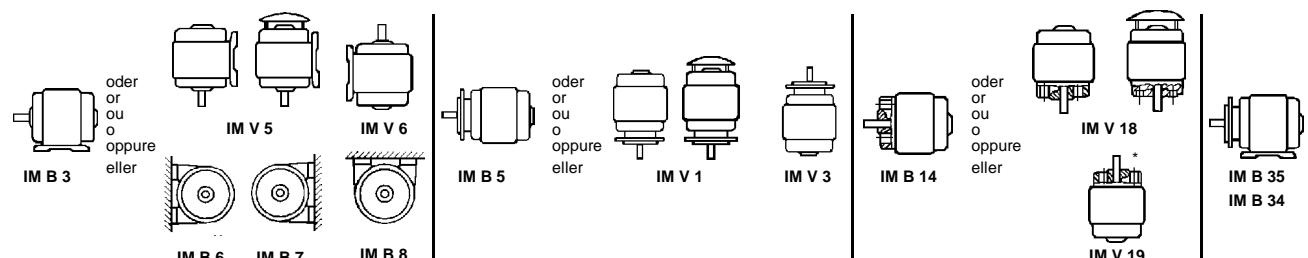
Bauformen / Types of construction / Formes de construction / Formas constructivas / Forme costruttive / Monteringssätt
